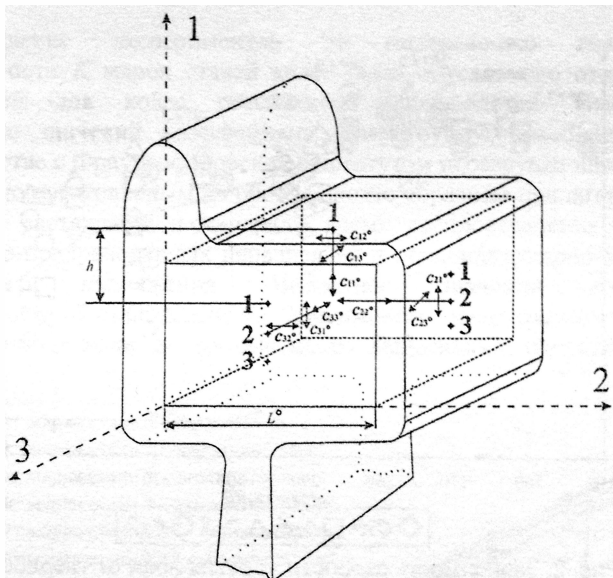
Образец – параллелепипед, изготовленный из сектора обода колеса
